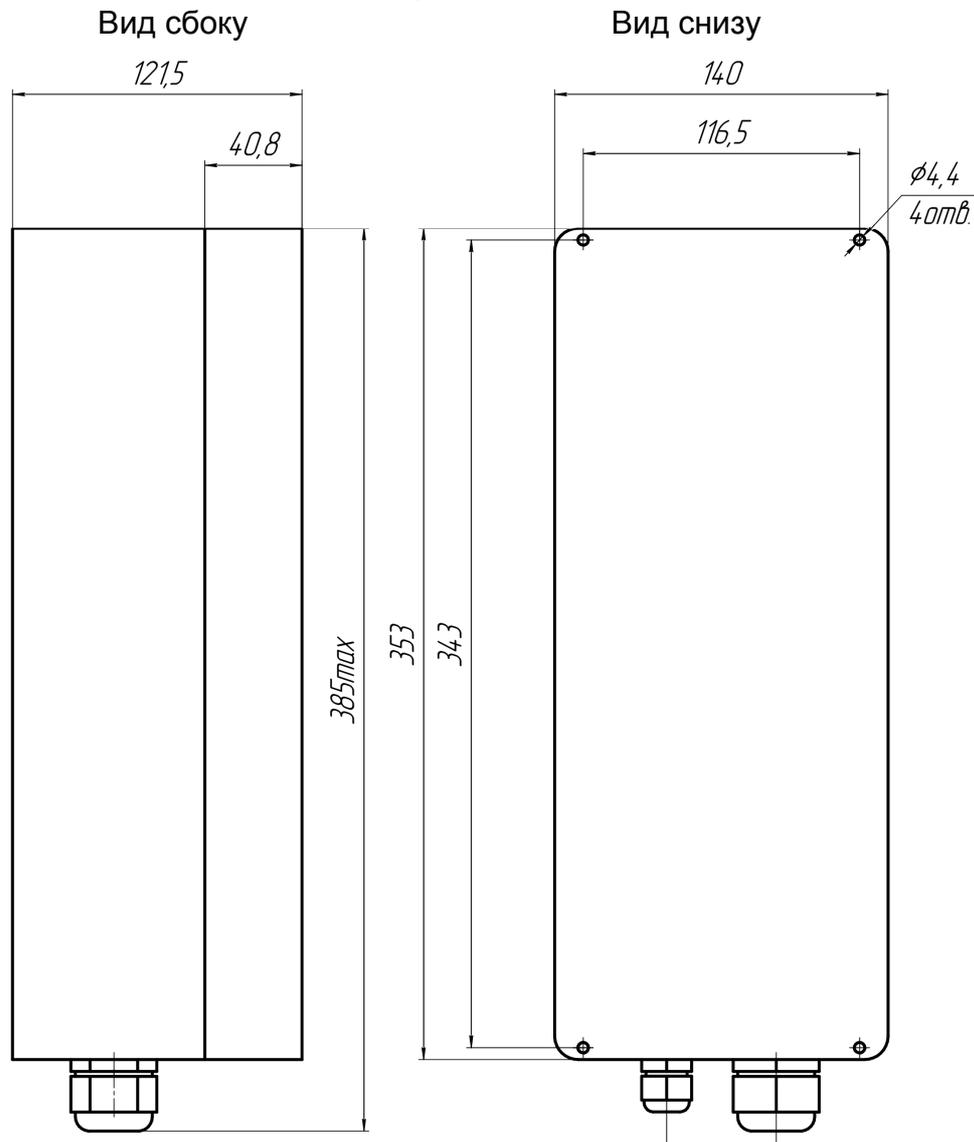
Габаритные размеры и размеры монтажных отверстий
